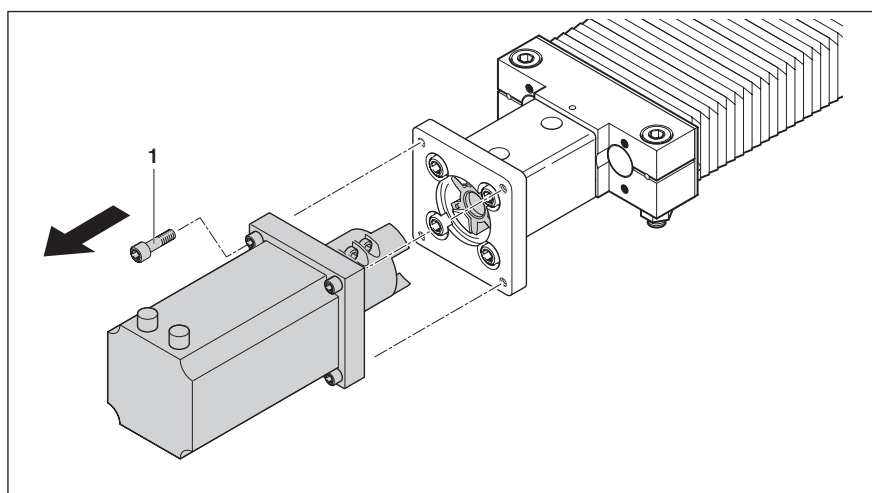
Motor demontieren / Flansch und Steckkupplung
